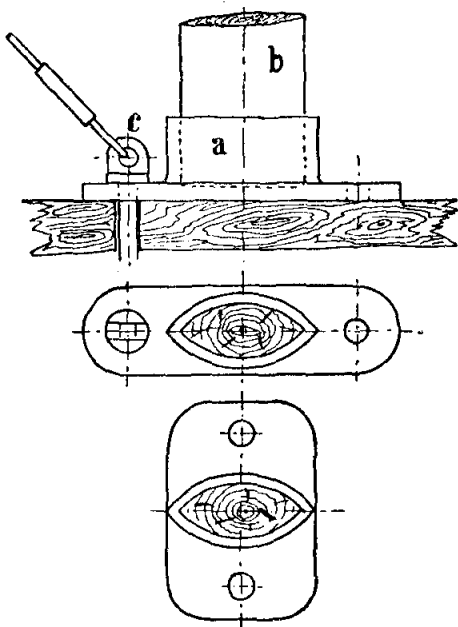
Алюминіевые отливки частей летательныхъ аппаратовъ Вуазена.
